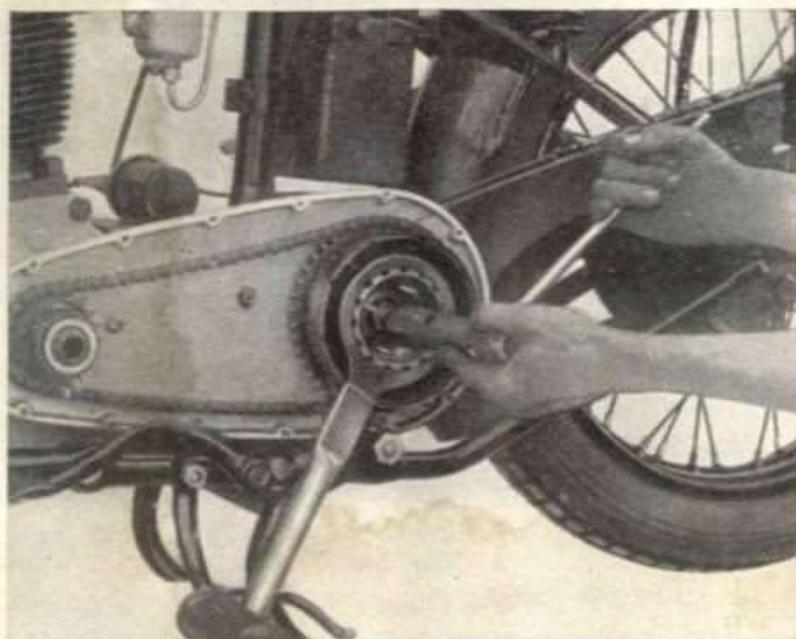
A 4 Utensili per smontaggio dado fissaggio coppa porta dischi
